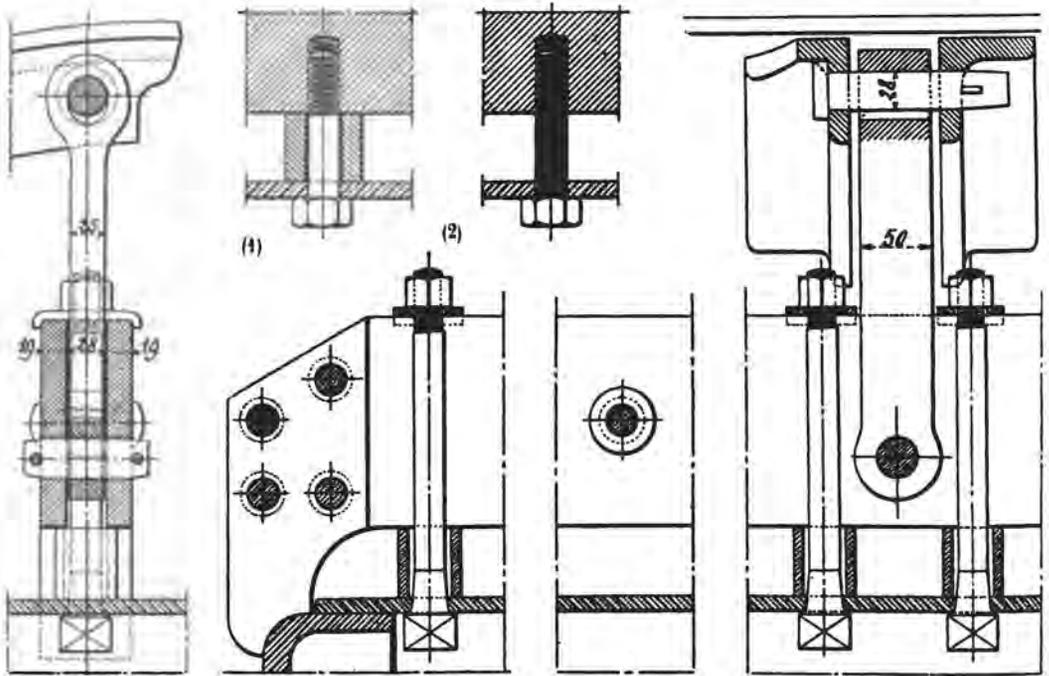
Fermes à deux flasques avec suspension ; les boulons fixant le ciel aux poutrelles ne sont pas vissés dans la plaque. Disposition anglaise.
